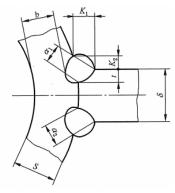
气体保护焊 、焊条电弧焊钢管与鳍片焊接熔深
